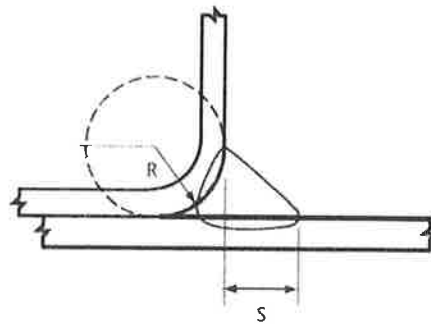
Exemple d'une soudure d'angle sur préparation en demi-V à bord tombé dans un assemblage en T
